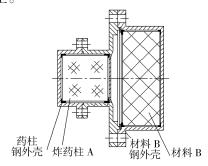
含炸药组合件 Fig.1 Explosive-containing assembly
